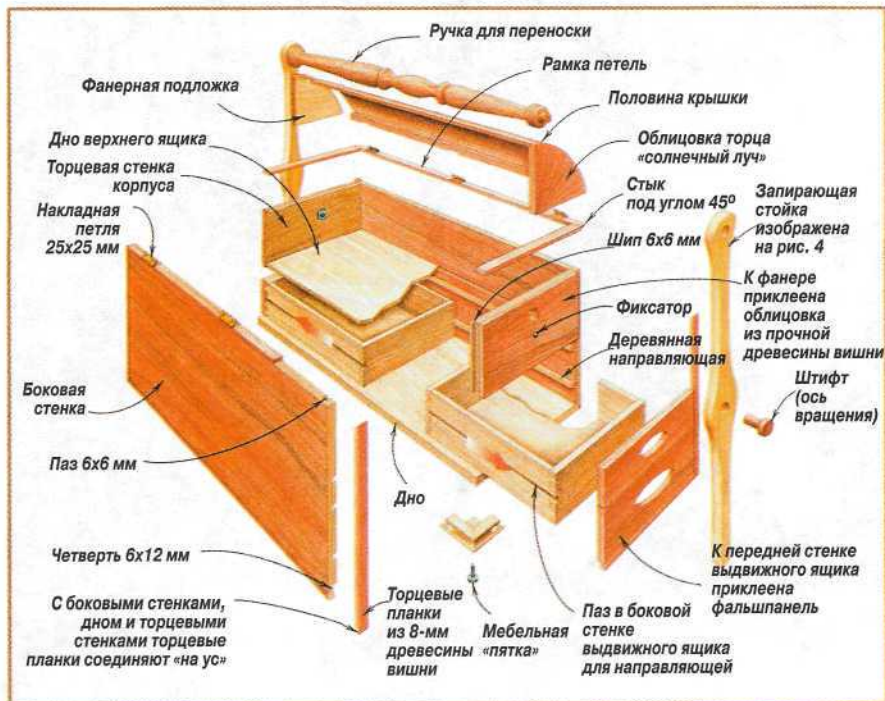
Корпус инструментального ящика сделан из фанеры древесины вишни. Крышка - бочкообразная, состоит из двух половинок. Ручка выточена из заготовки, склеенной из древесины вишни и клена. В верхнем положении стойки ручки фиксируют выдвижные ящики в закрытом положении. Повернув ручку вниз, можно открыть крышку и выдвинуть ящики.
